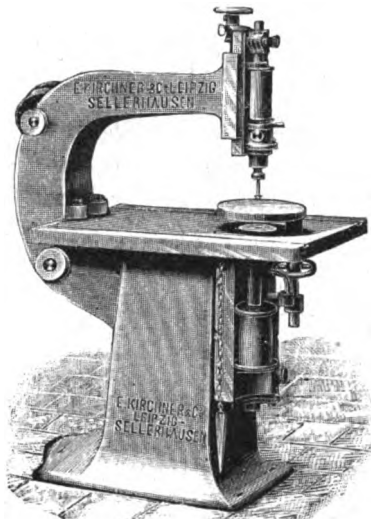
Universal-Fräsmaschine als Oberfräse.
